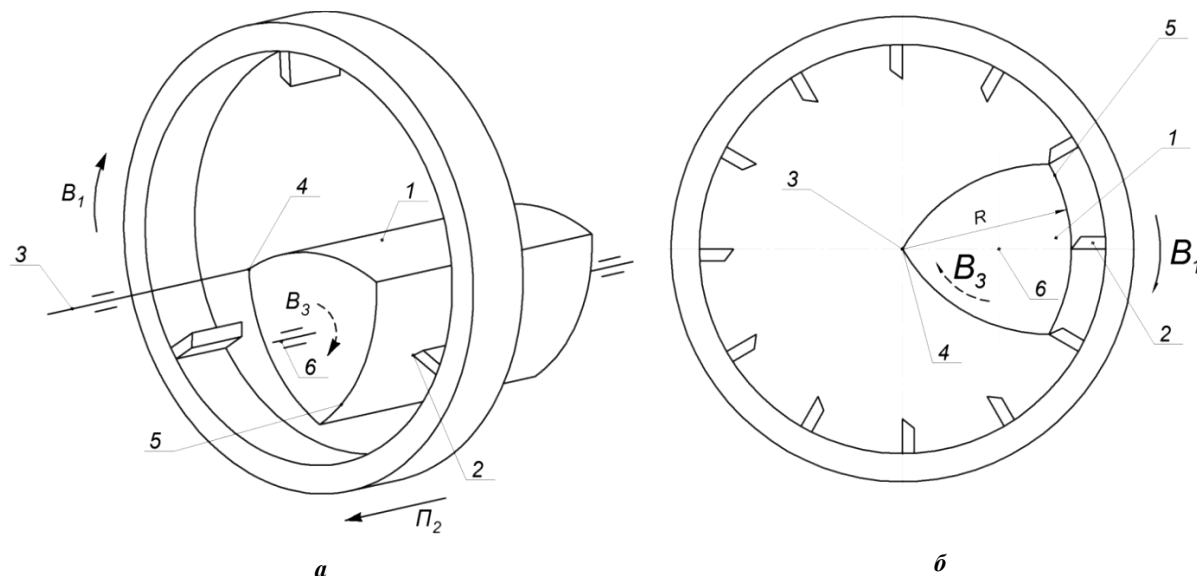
Кинематическая схема обработки (а) и схема формирования профиля детали в виде треугольника Рело (б) охватываемой резцовой головкой
